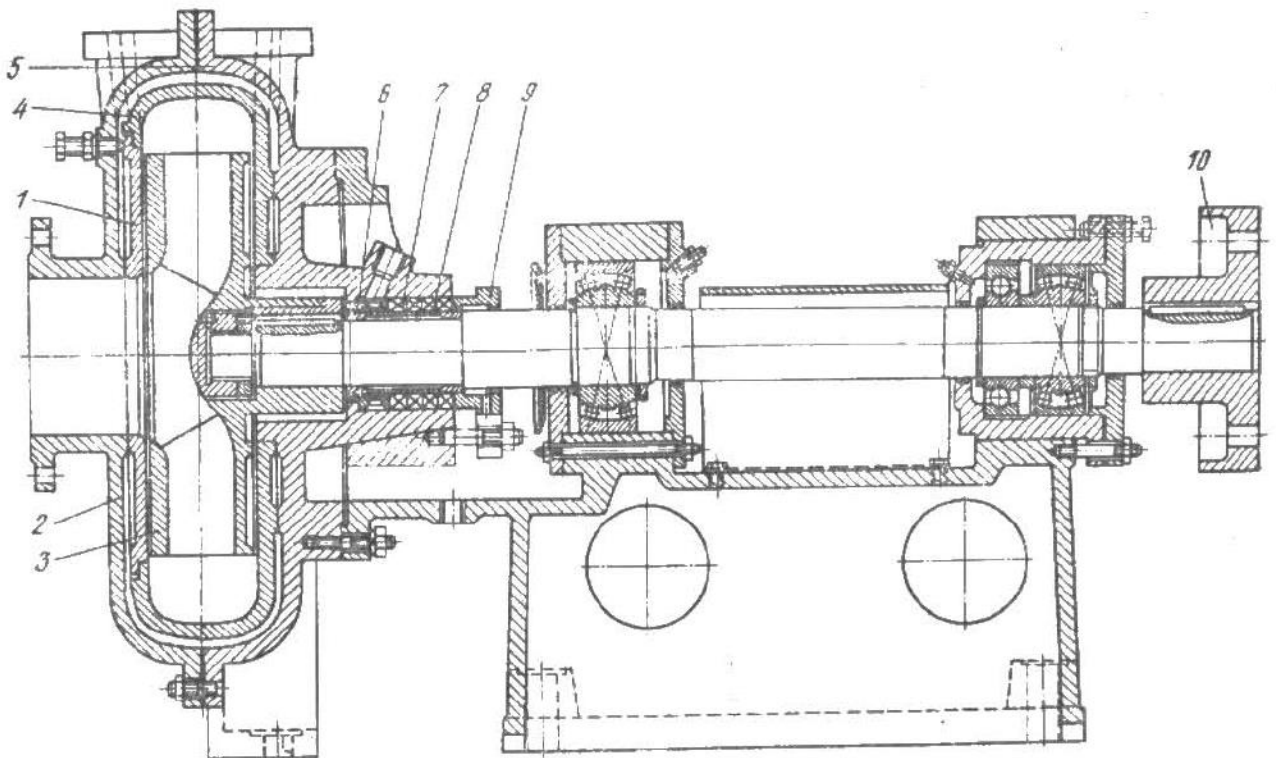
Насос відцентровий ґрунтовий 8Гр-8Т [8]: 1 - футерування всмоктувальної кришки; 2 - передня половина корпусу; 8 - робоче колесо; 4 - внутрішній корпус; 5 - задня половина корпусу; 6 - колесо сальника; 7 - набивання сальника; 8 - захисна втулка; 9 - кришка сальника; 10 - муфта
